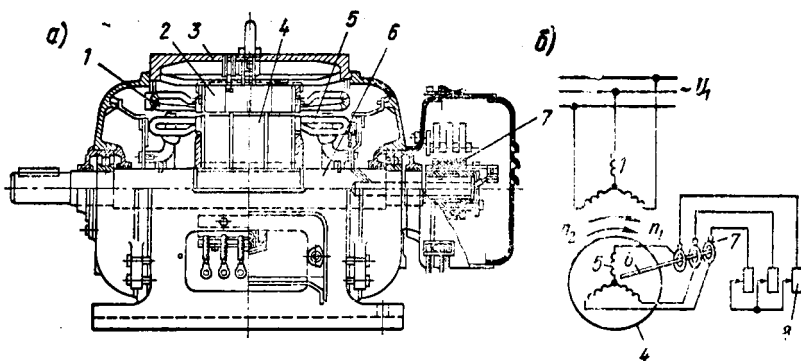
Асинхронный электродвигатель с фазным ротором: 1 — обмотка статора; 2 — сердечник статора; 3 — корпус (станина); 4 — сердечник ротора; 5 — обмотка ротора; 6 — вал ротора; 7 — контактные кольца; 8 — пусковой реостат
